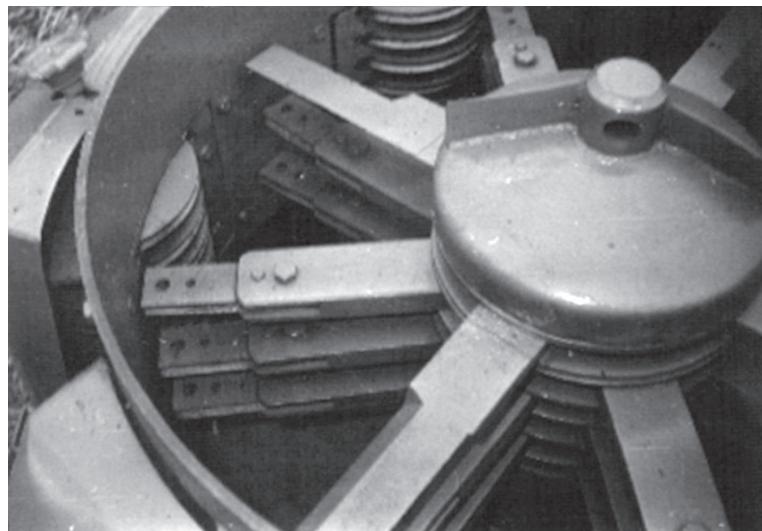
Измельчитель с установленными в державке двумя режущими ножами
